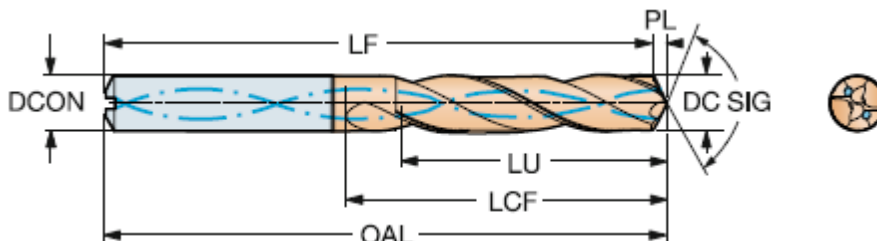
Сверло 860.1.1100-037A1-PM 4234
